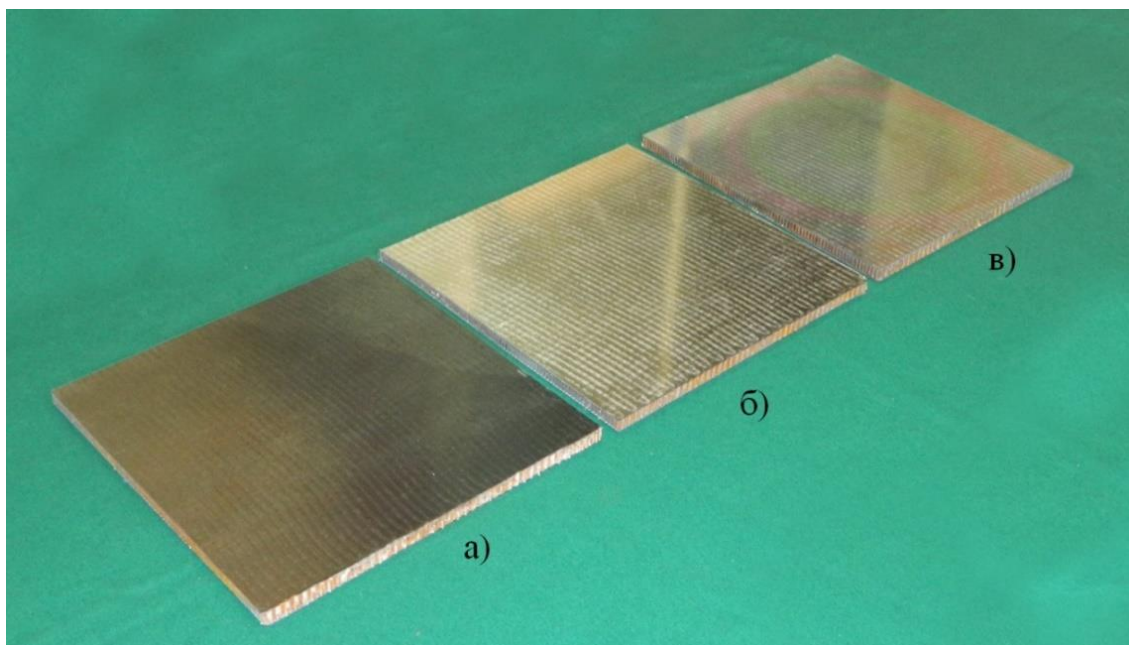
Углепластиковые факеты сотовой конструкции:
